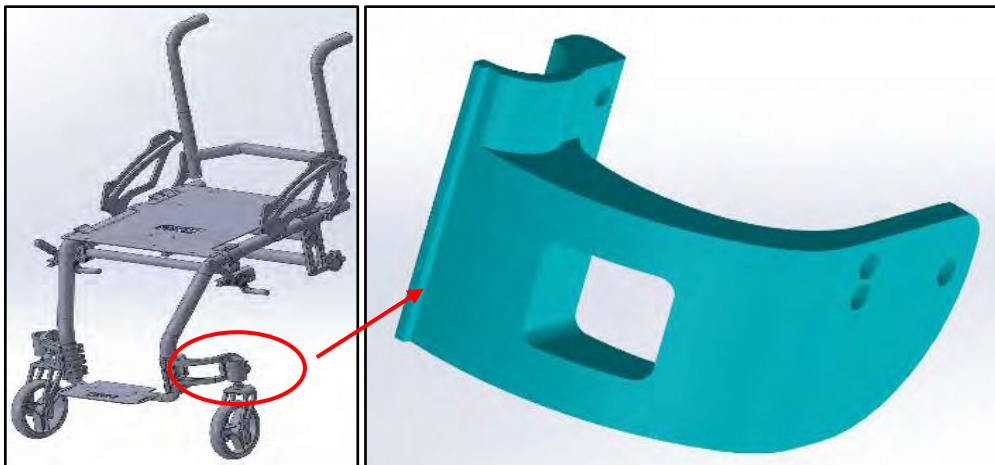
Diseño de silla de ruedas con detalle de ubicación de la pieza bajo estudio (Izquierda).Detalle de Brida Portarodamiento Original (Derecha).
